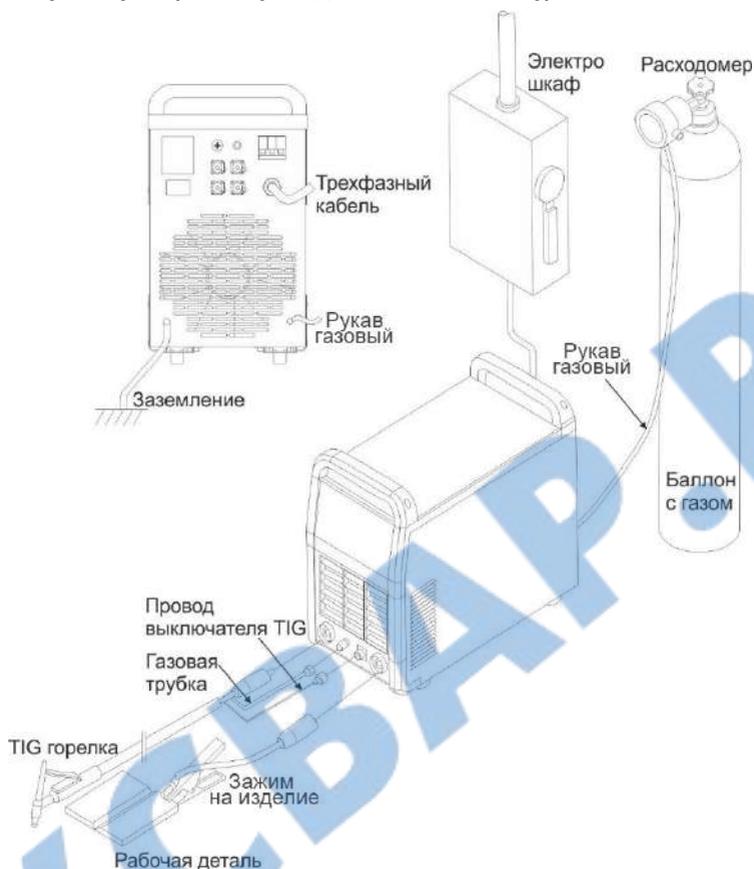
Установка сварочного аппарата TIG (стандартная схема для данного сварочного аппарата)
